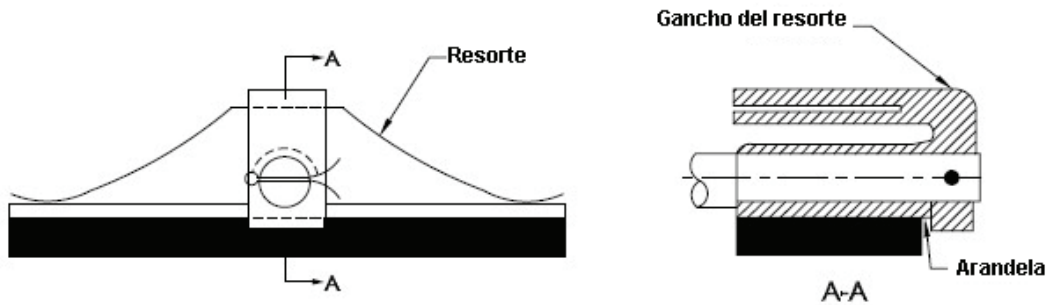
Gancho del resorte y resorte para impedir la rotación de la zapata
